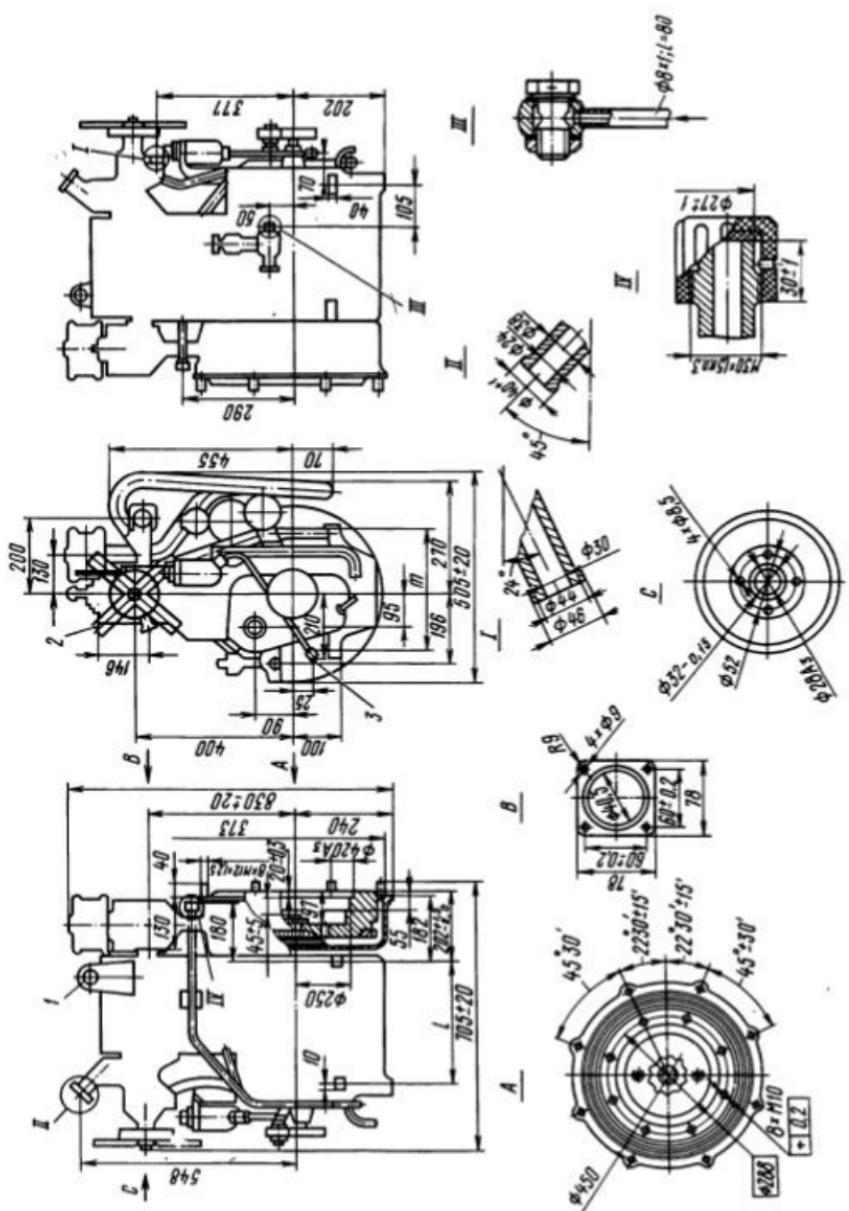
Габаритный чертеж дизеля 2Ч 8,5/11 (1Р2-7,5 и 2Р2-7,5):
